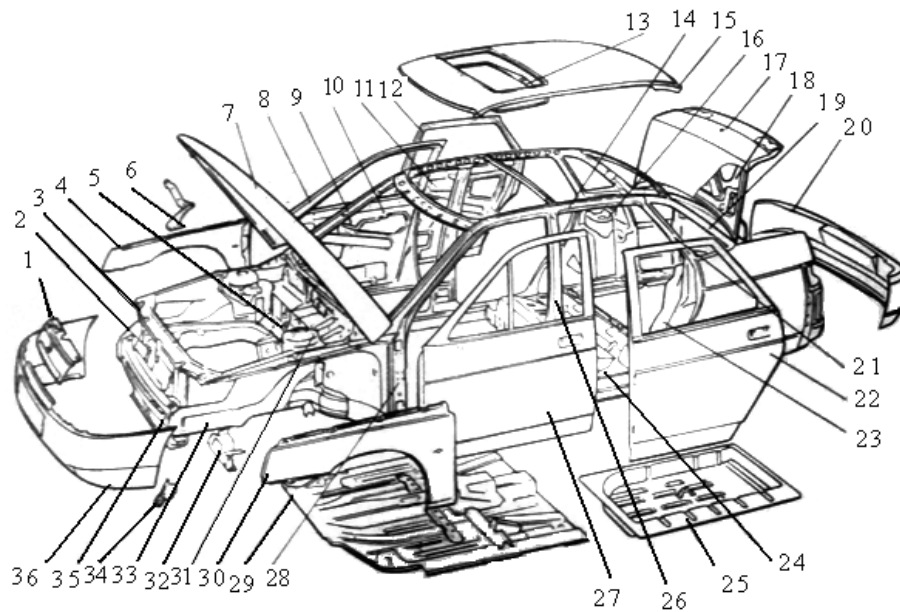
Конструкція каркаса кузова: 1 – облицювання радіатора; 2 – рама радіатора; 3 – горішня поперечка рами радіатора; 4, 30 – крило; 5 – щиток передньої частини; 6 – петля капоту; 7 – капот; 8, 12, 22, 27 – двері; 9 – стійка лобового скла; 10, 11 – внутрішня панель дверей; 13 – рамка люка даху; 14 – боковина; 15 – панель даху; 16 – опора пружини задньої підвіски; 17 – кришка багажника; 18 - внутрішня панель кришки багажника; 19 – рамка вікна боковини; 20 – задній бампер; 21, 28 – стійка; 23 – арка заднього колеса; 24 – середня підлога; 25 – ніша запасного колеса; 26 – центральна стійка; 29- передня підлога; 31 – опора пружини передньої підвіски; 32 – кронштейн; 33 – передній лонжерон; 34 – кронштейн вушка для буксирування; 35 – панель передка; 36 – передній бампер [1].
